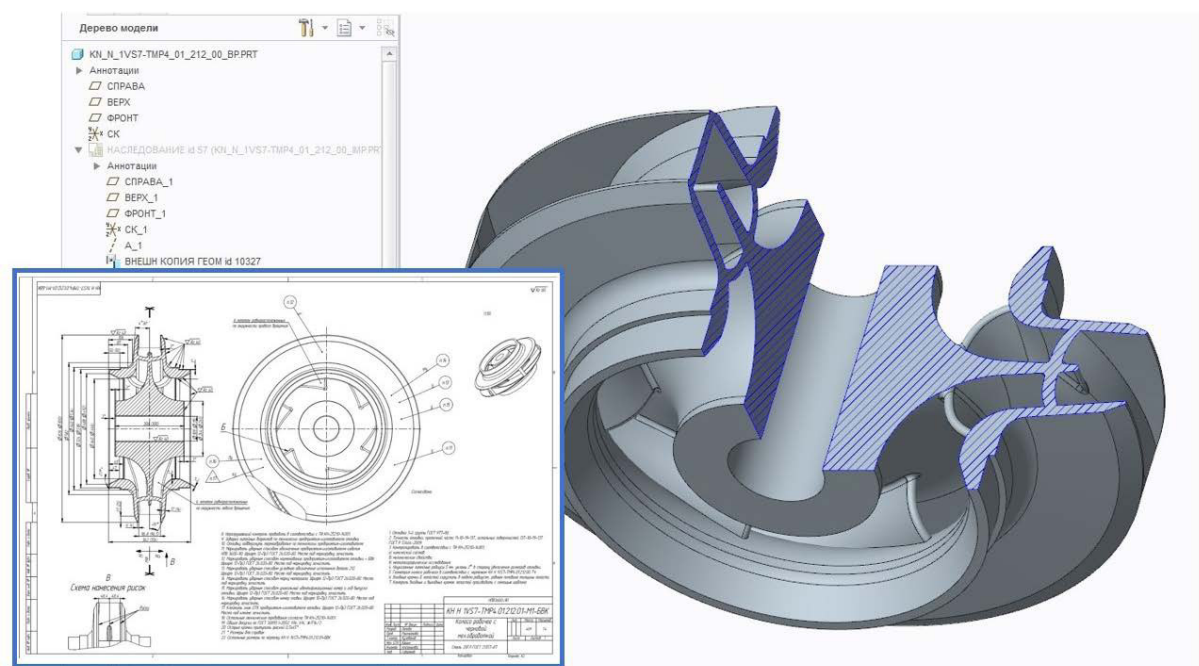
3D-модель и чертёж рабочего колеса с предварительной обработкой
